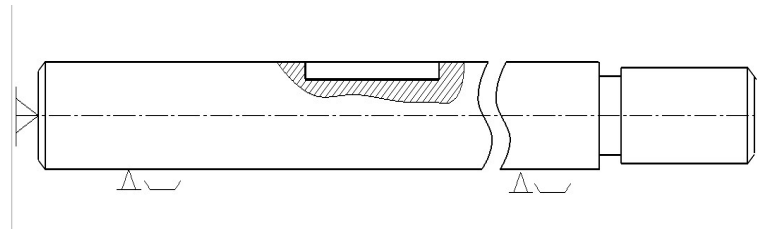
Схема базування при фрезерній обробці шпонки
